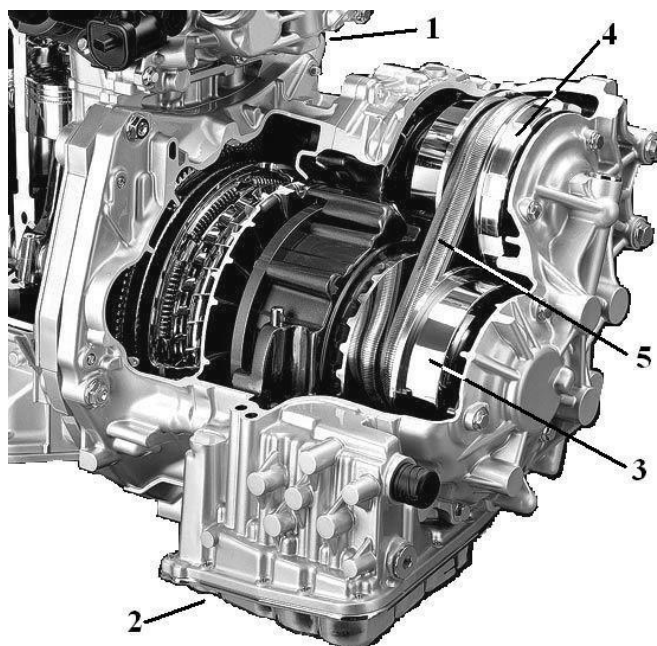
Коробка передач с клиноременным вариатором:
